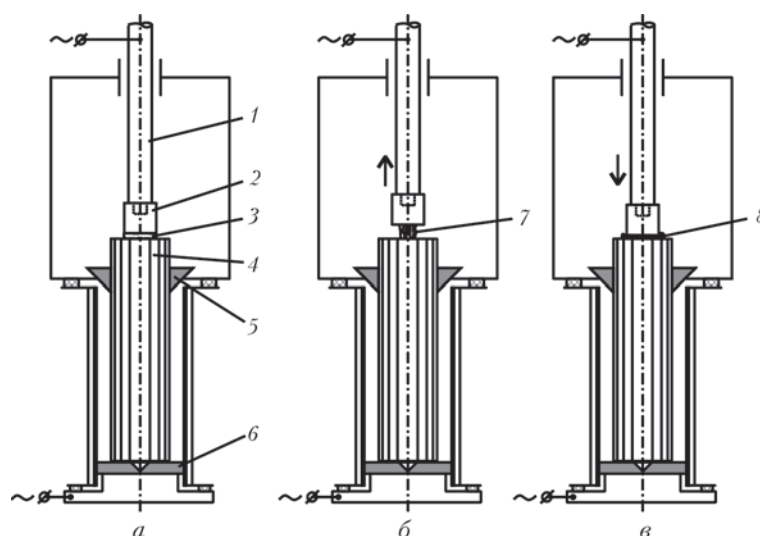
Схема приварки инвентарной головки к расходуемому электроду (*а* — нагрев соединяемых поверхностей проходящим током; *б* — оплавление поверхностей электрической дугой; *в* — осадка): 1 — шток вертикального перемещения электрода; 2 — инвентарная головка; 3 — токопроводящая прослойка; 4 — расходный электрод; 5, 6 — центрирующие втулки; 7 — электрическая дуга; 8 — сварное соединение
